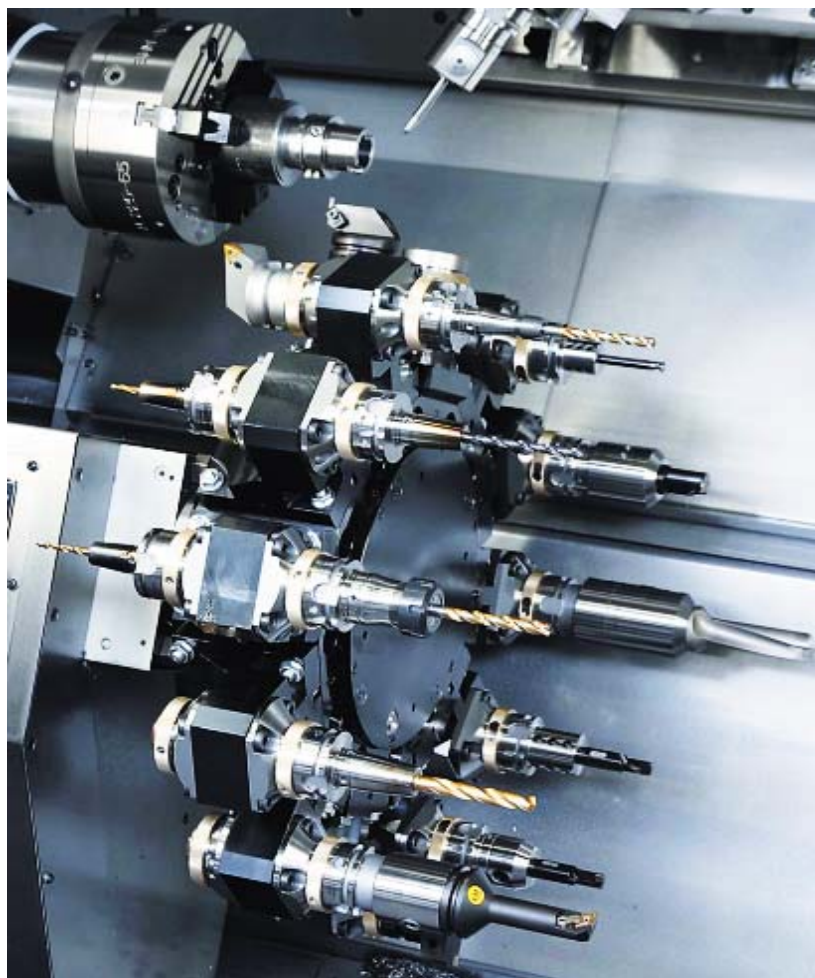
Монолитные твердосплавные осевые инструменты компании Morse Cutting Tools
